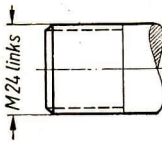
Bemaßungsbeispiel für Linksgewinde
